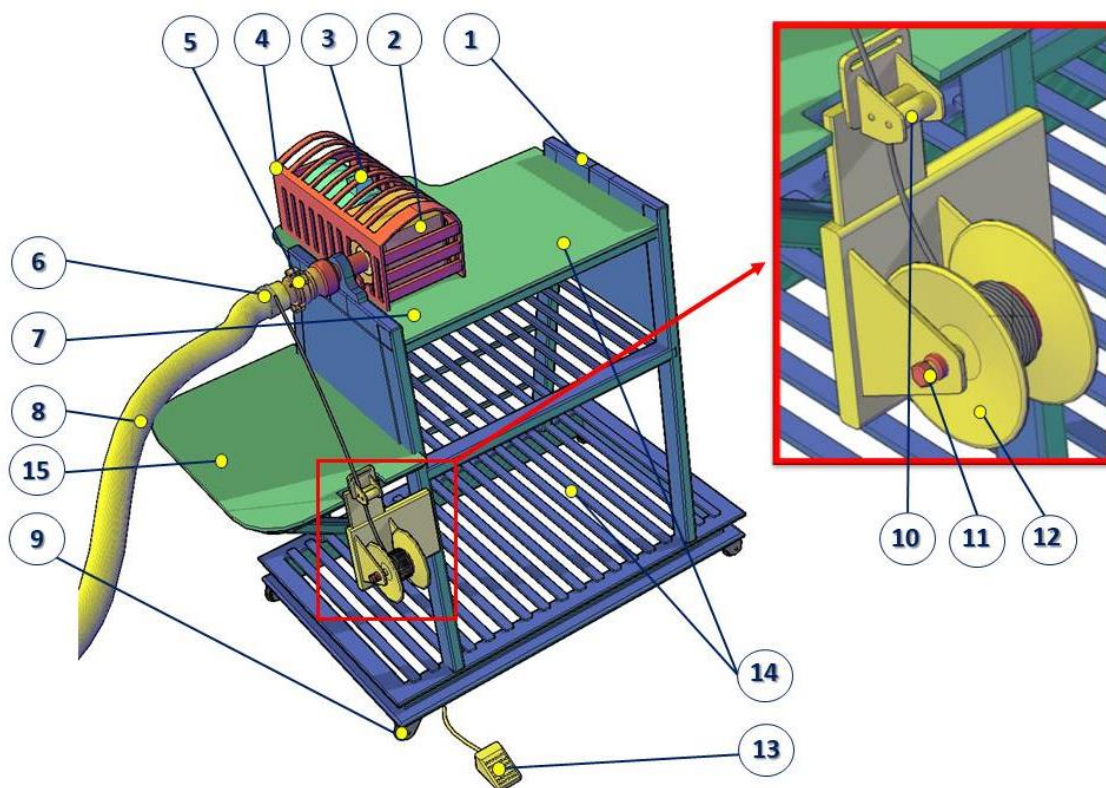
Габаритные размеры станка для навязки пожарных рукавов на соединительные головки
